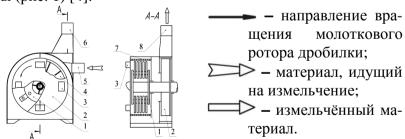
Молотковая дробилка с торцевыми вихревыми камерами: 1 — молотковый ротор; 2 — крышка дробильной камеры; 3 — вихревая камера; 4 — вентилятор; 5 — загру-
